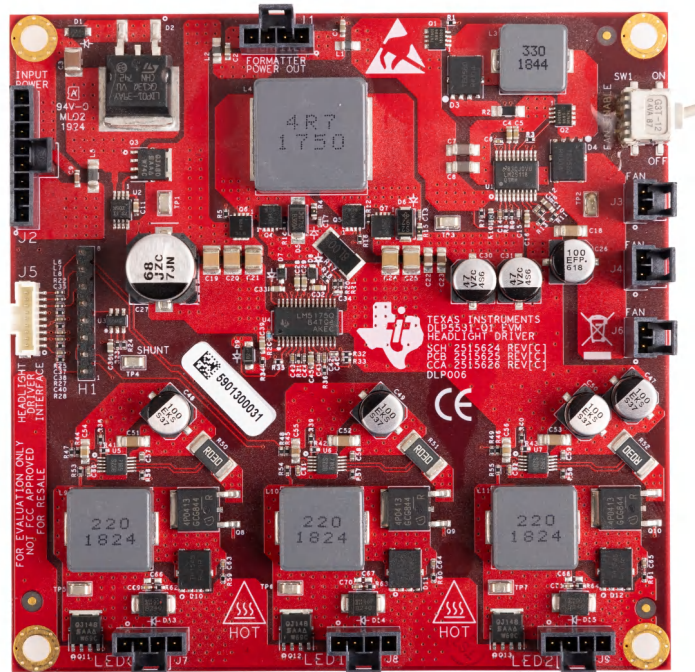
LED 驱动器 PCB - DLP4621Q1EVM
